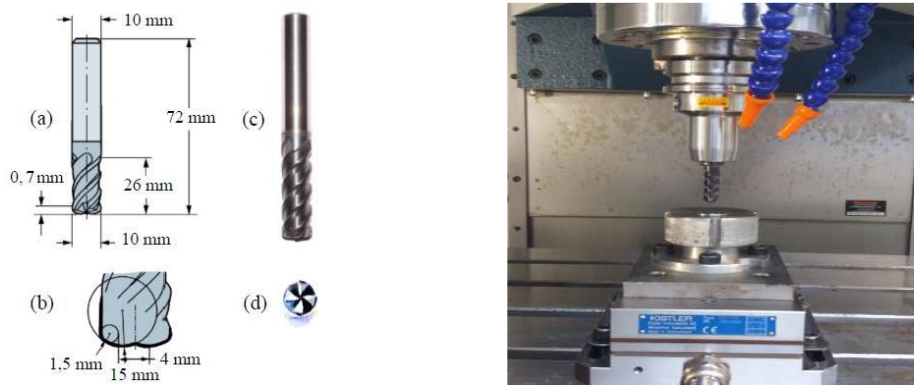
Setup experimental (a) dimensões; (b) detalhe duplo raio de ponta; (c) foto periferia; (d) foto frontal e Setup experimental.
